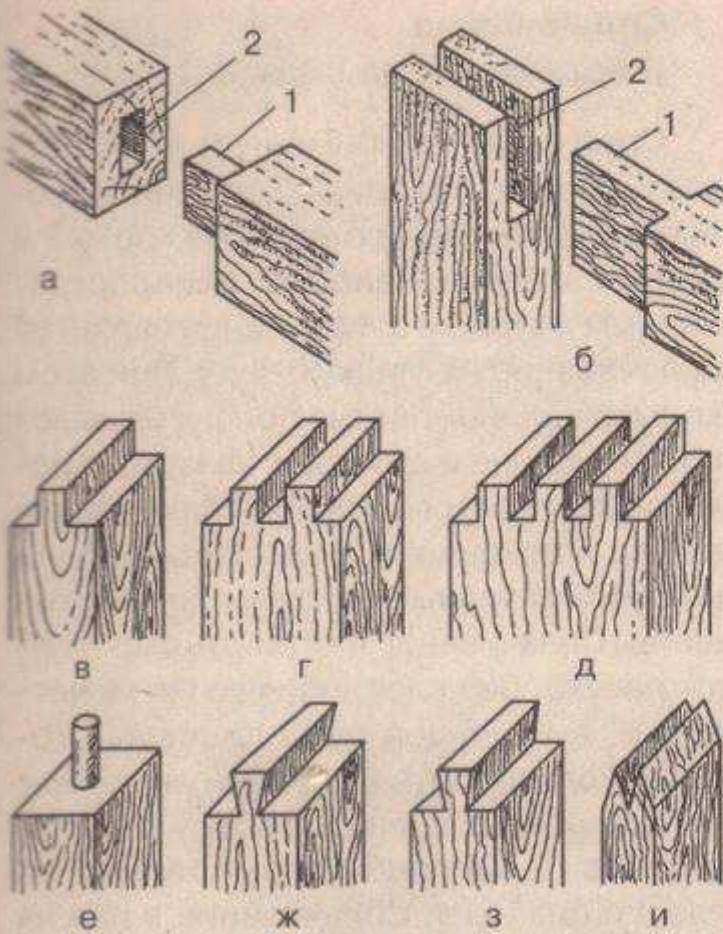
Простейшие шиповые соединения и виды шипов: а — в гнездо; б — в проушину; 1 — шип; 2 — гнездо, проушина; в — одинарный шип; г — двойной шип; д — многократный шип; е — круглый шип; ж — шип «ласточкин хвост»; з — односторонний шип; и — зубчатый шип
